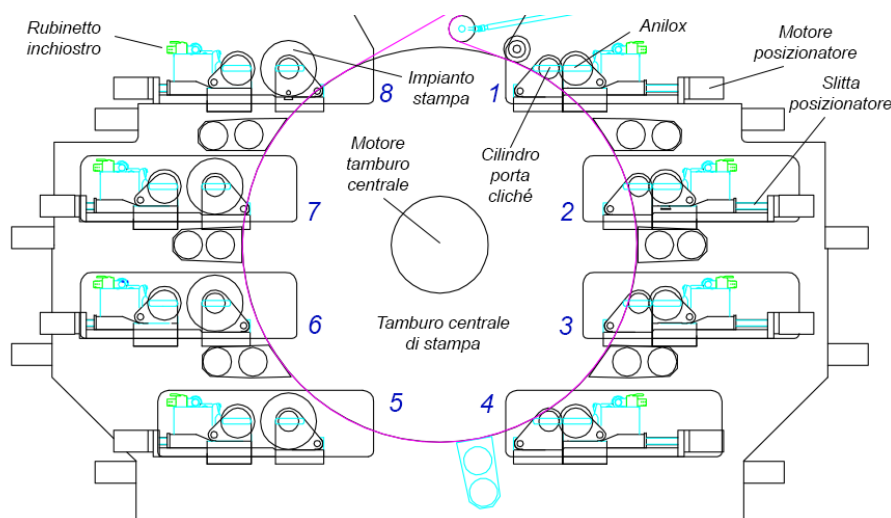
Disegno CAD di un gruppo stampa ad 8 stazioni.
